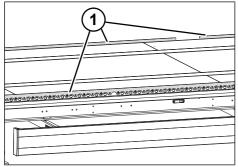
Multi Screw am Multi Lock-Außenrahmen
